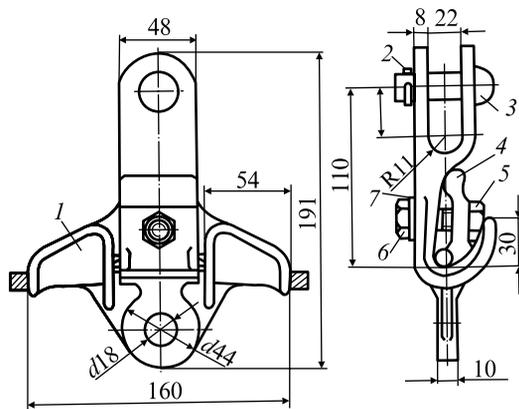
Одинарное седло: 1 — седло; 2 — шплинт; 3 — валик  $d = 16$  мм; 4 — планка с резьбой; 5 — гайка М12; 6 — болт М12×45; 7 — шайба
